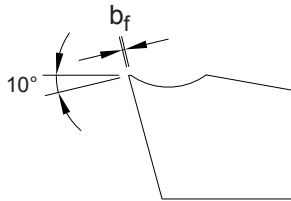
Neutrale openingshoek voor afwerking en voorbereiding
